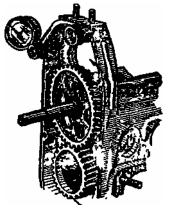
Измерение бокового зазора в зацеплении зубчатых колес распределения
